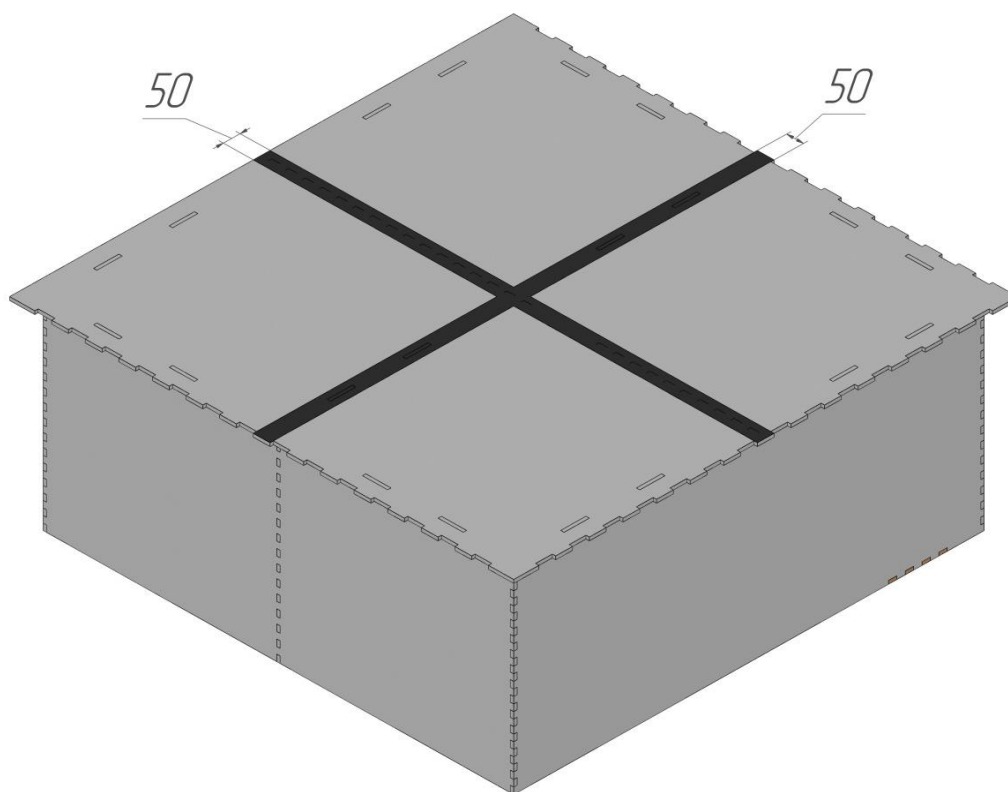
Промежуточная платформа (габаритные размеры)
